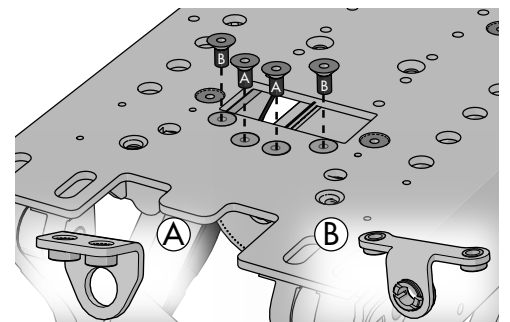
Es gibt verschiedene Bohrungen für die Schrauben, die je nach Halterungsversion variieren.
